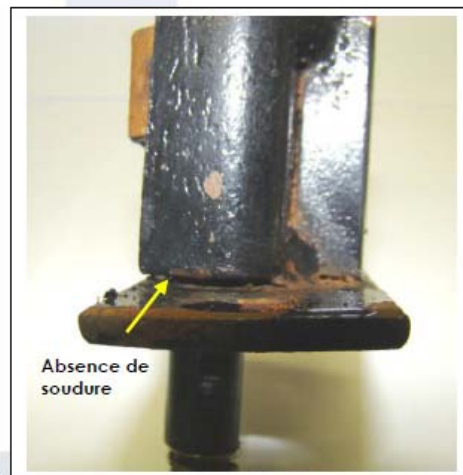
Vue latérale de la soudure partielle à la base de l'ancien modèle de barrure de 2003.
